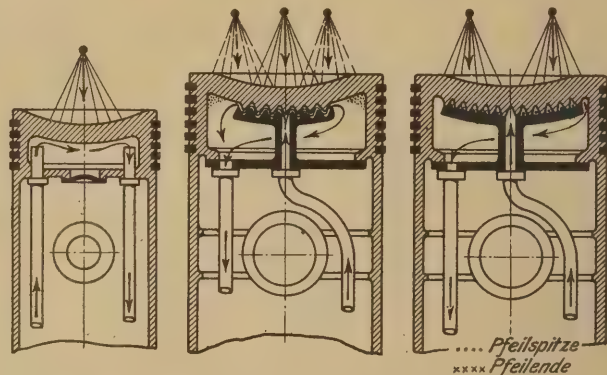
bis 8. Schmierung einer ortsfesten Dieselmotorenmaschine.
